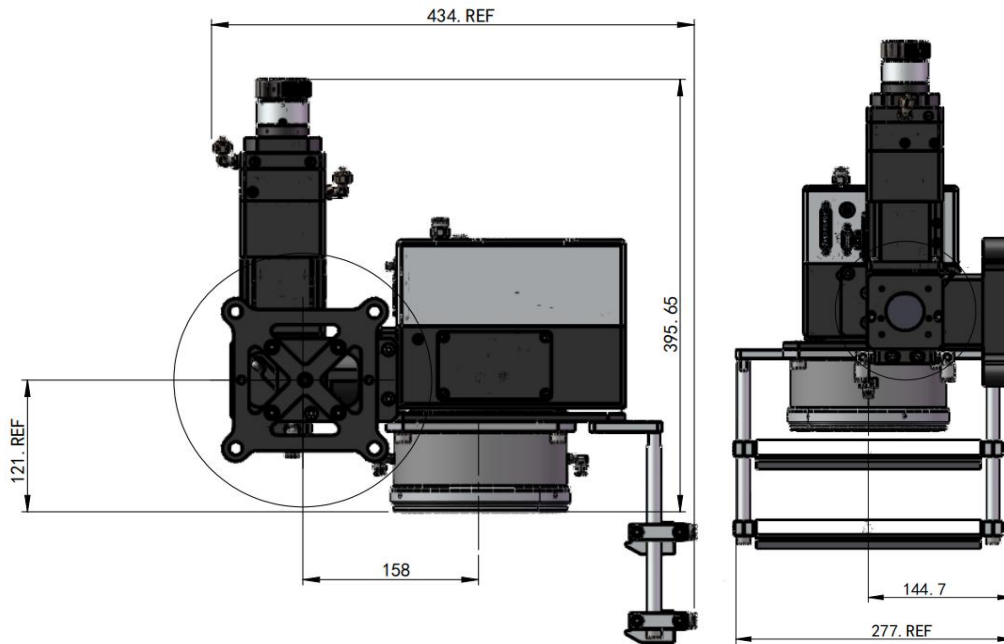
焊接模组尺寸 (单位: mm)
